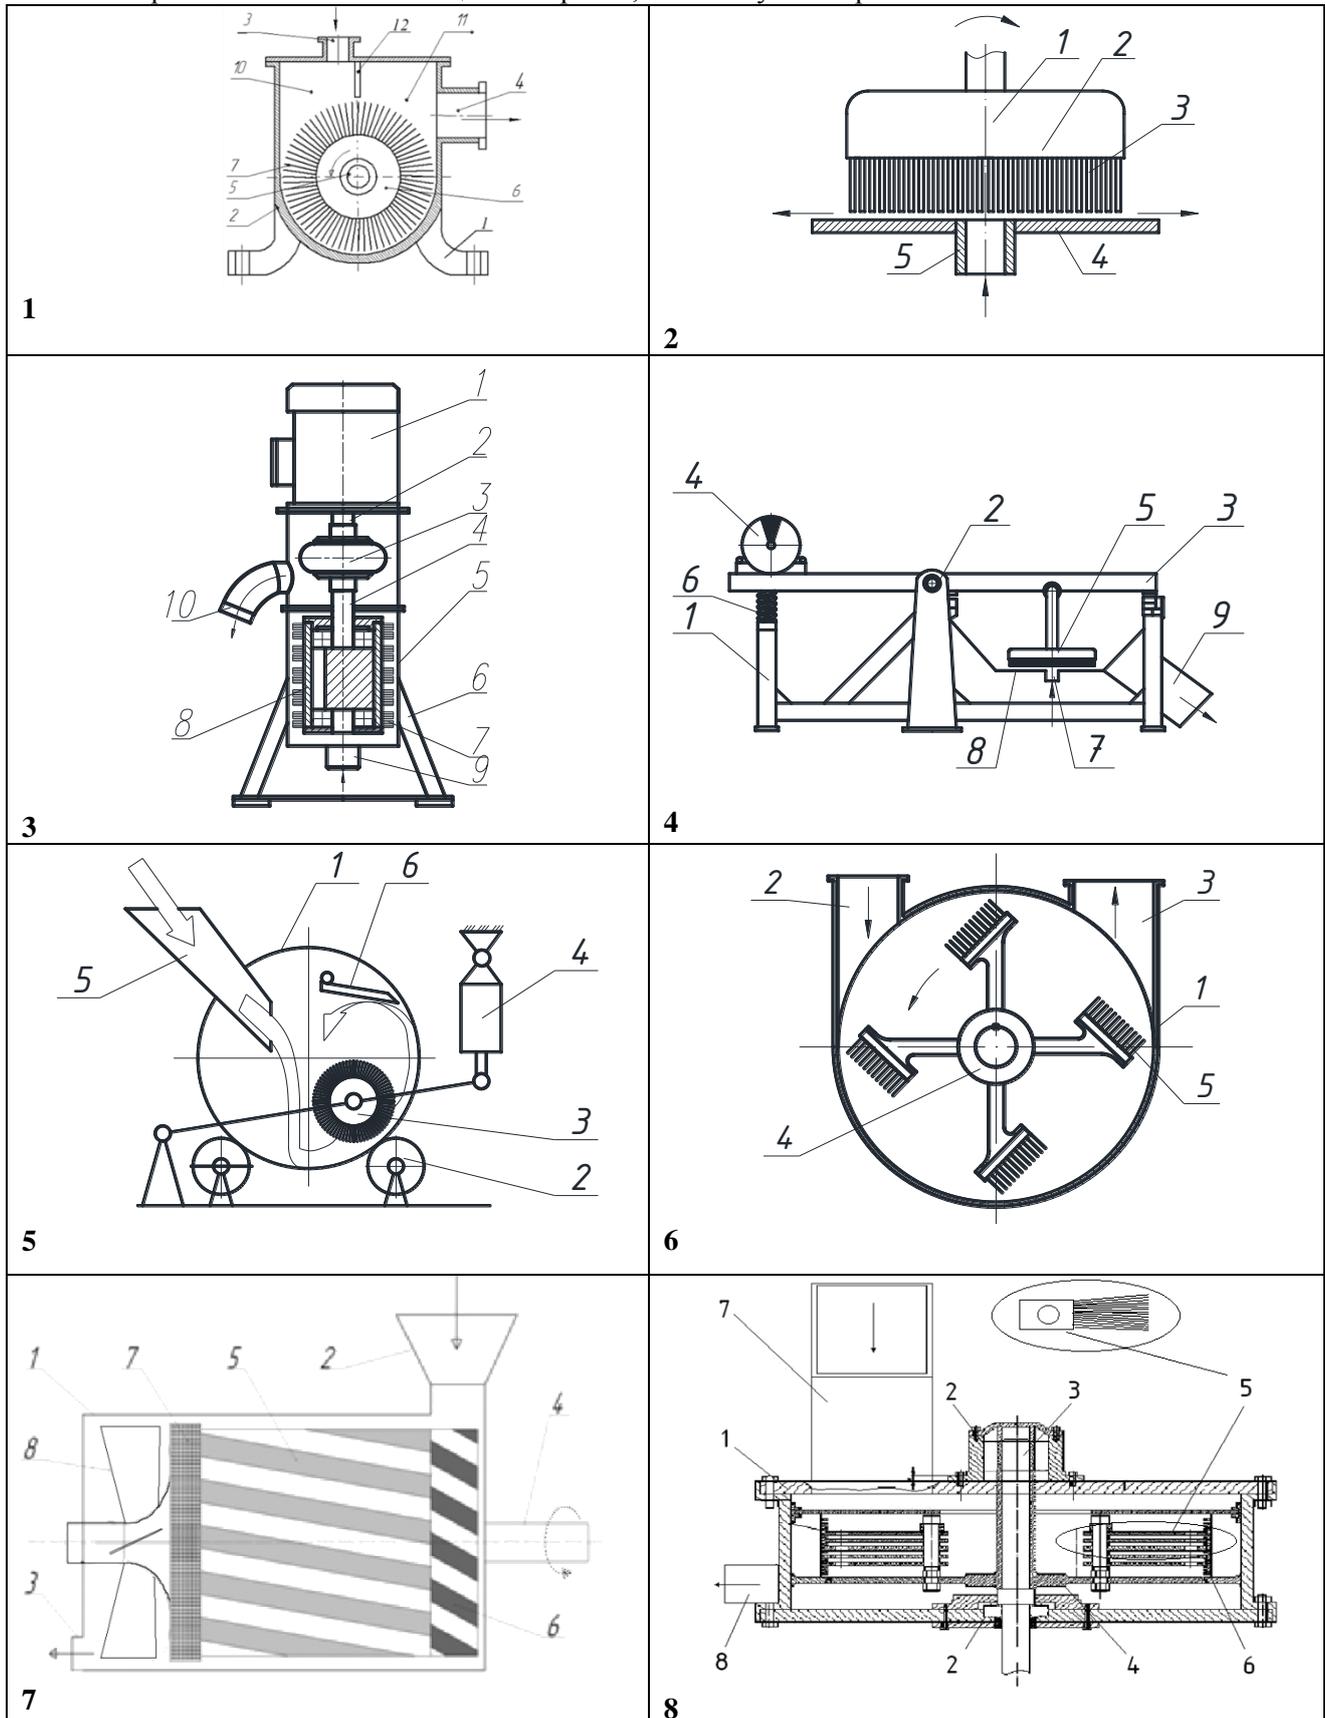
Варианты конструкций измельчителей с игольфрезерными рабочими органами
